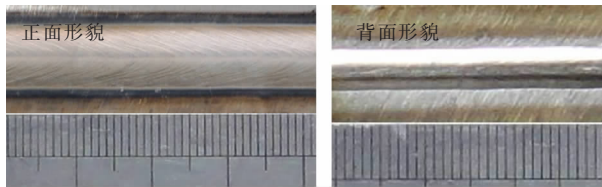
10 mm 厚不锈钢板 DP-TIG 焊接形貌
